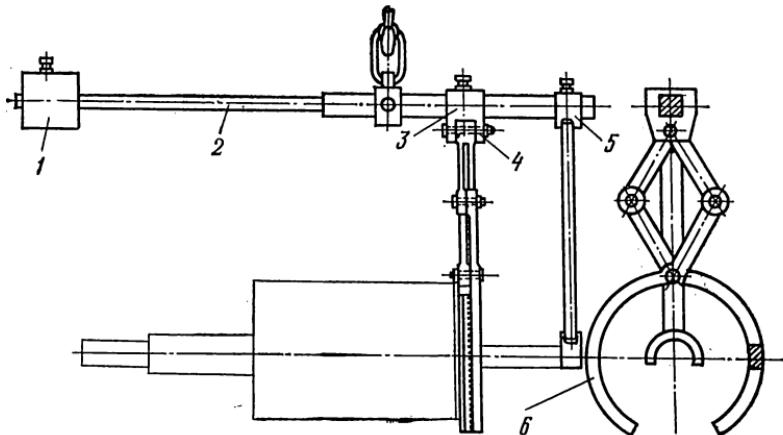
Приспособление для вывода ротора из статора и ввода в него:
